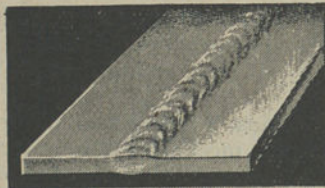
Aspecto e corte duma boa soldadura.
